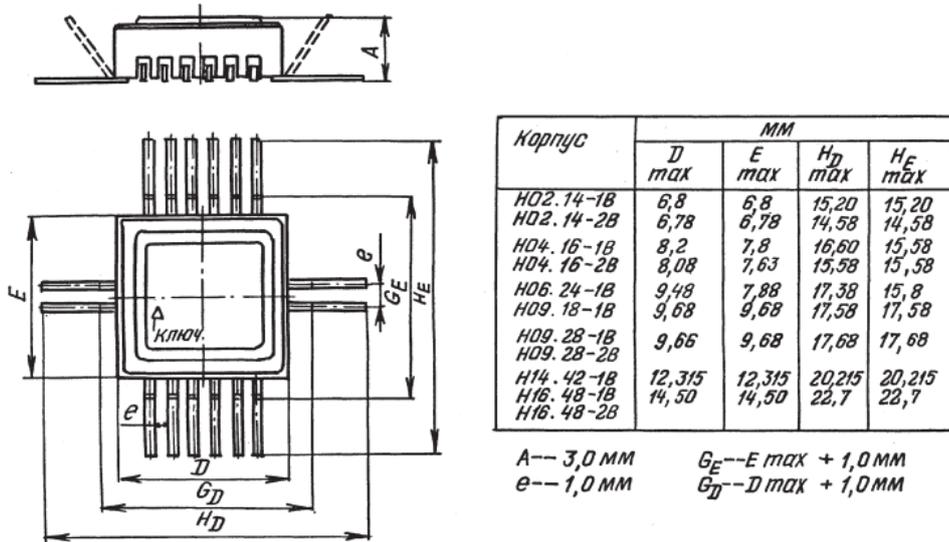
Габаритный чертеж корпуса H09.18-1B
